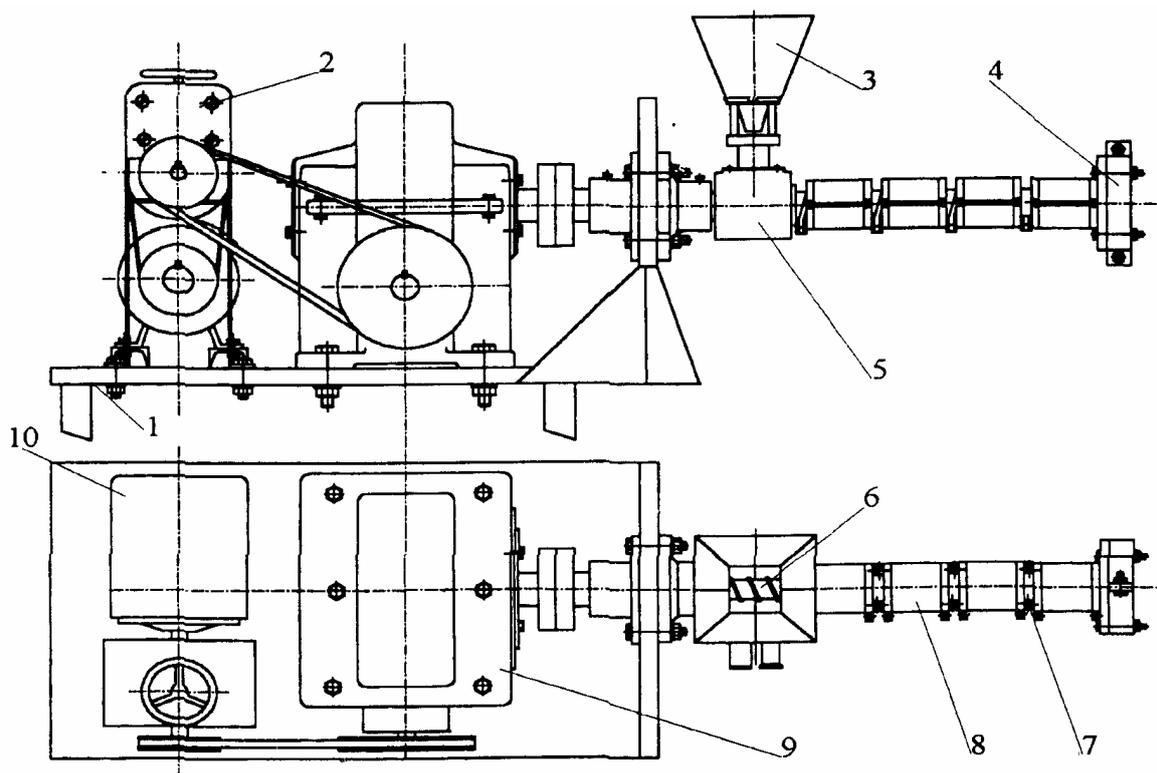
Конструктивная схема одношнекового экструдера (по А.Н. Острикову [20]): 1 – станина; 2 – вариатор; 3 – загрузочный бункер; 4 – матрица; 5 – корпус; 6 – шнек; 7 – система охлаждения; 8 – электронагреватели; 9 – редуктор; 10 – электродвигатель
